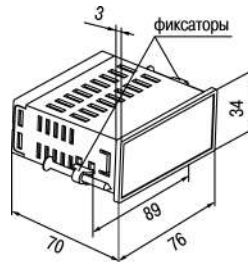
Габаритные размеры корпуса ЩЗ
